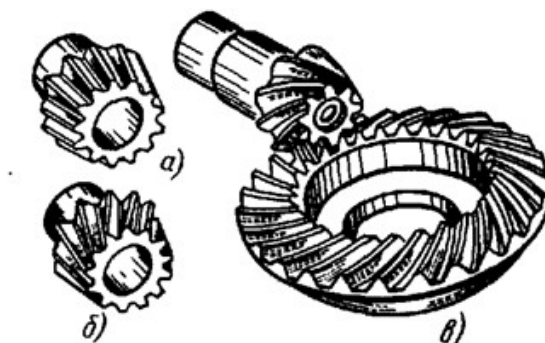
Конические зубчатые колеса: а) с прямыми; б) с косыми; в) с круговыми зубьями
